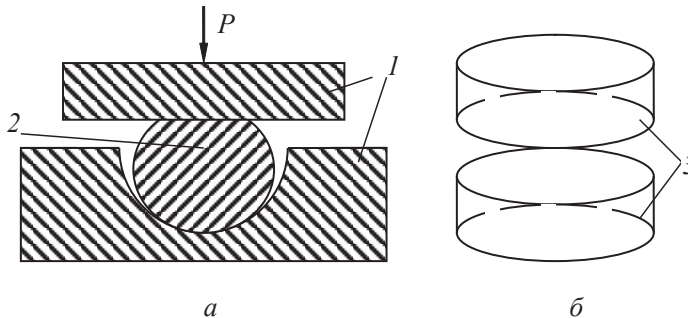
Схема получения разъемных образцов: а — штамповка полуцилиндра: 1 — штамповая оснастка; 2 — заготовка; б — сборка дисков: 3 — дисковые образцы
